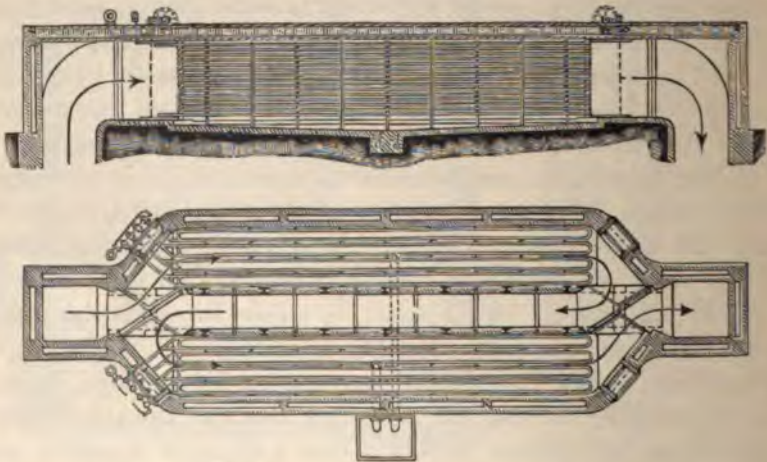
Längenschnitt, Grundriss und Querschnitt eines Kühlapparates.
